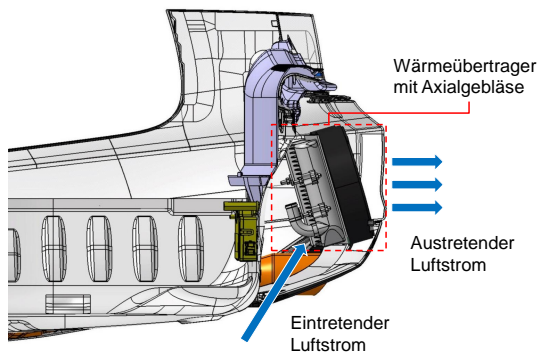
Integration eines Rückkühlers mit Axialgebläse im Bereich des Heckstoßfängers einer Audi A6-Limousine
